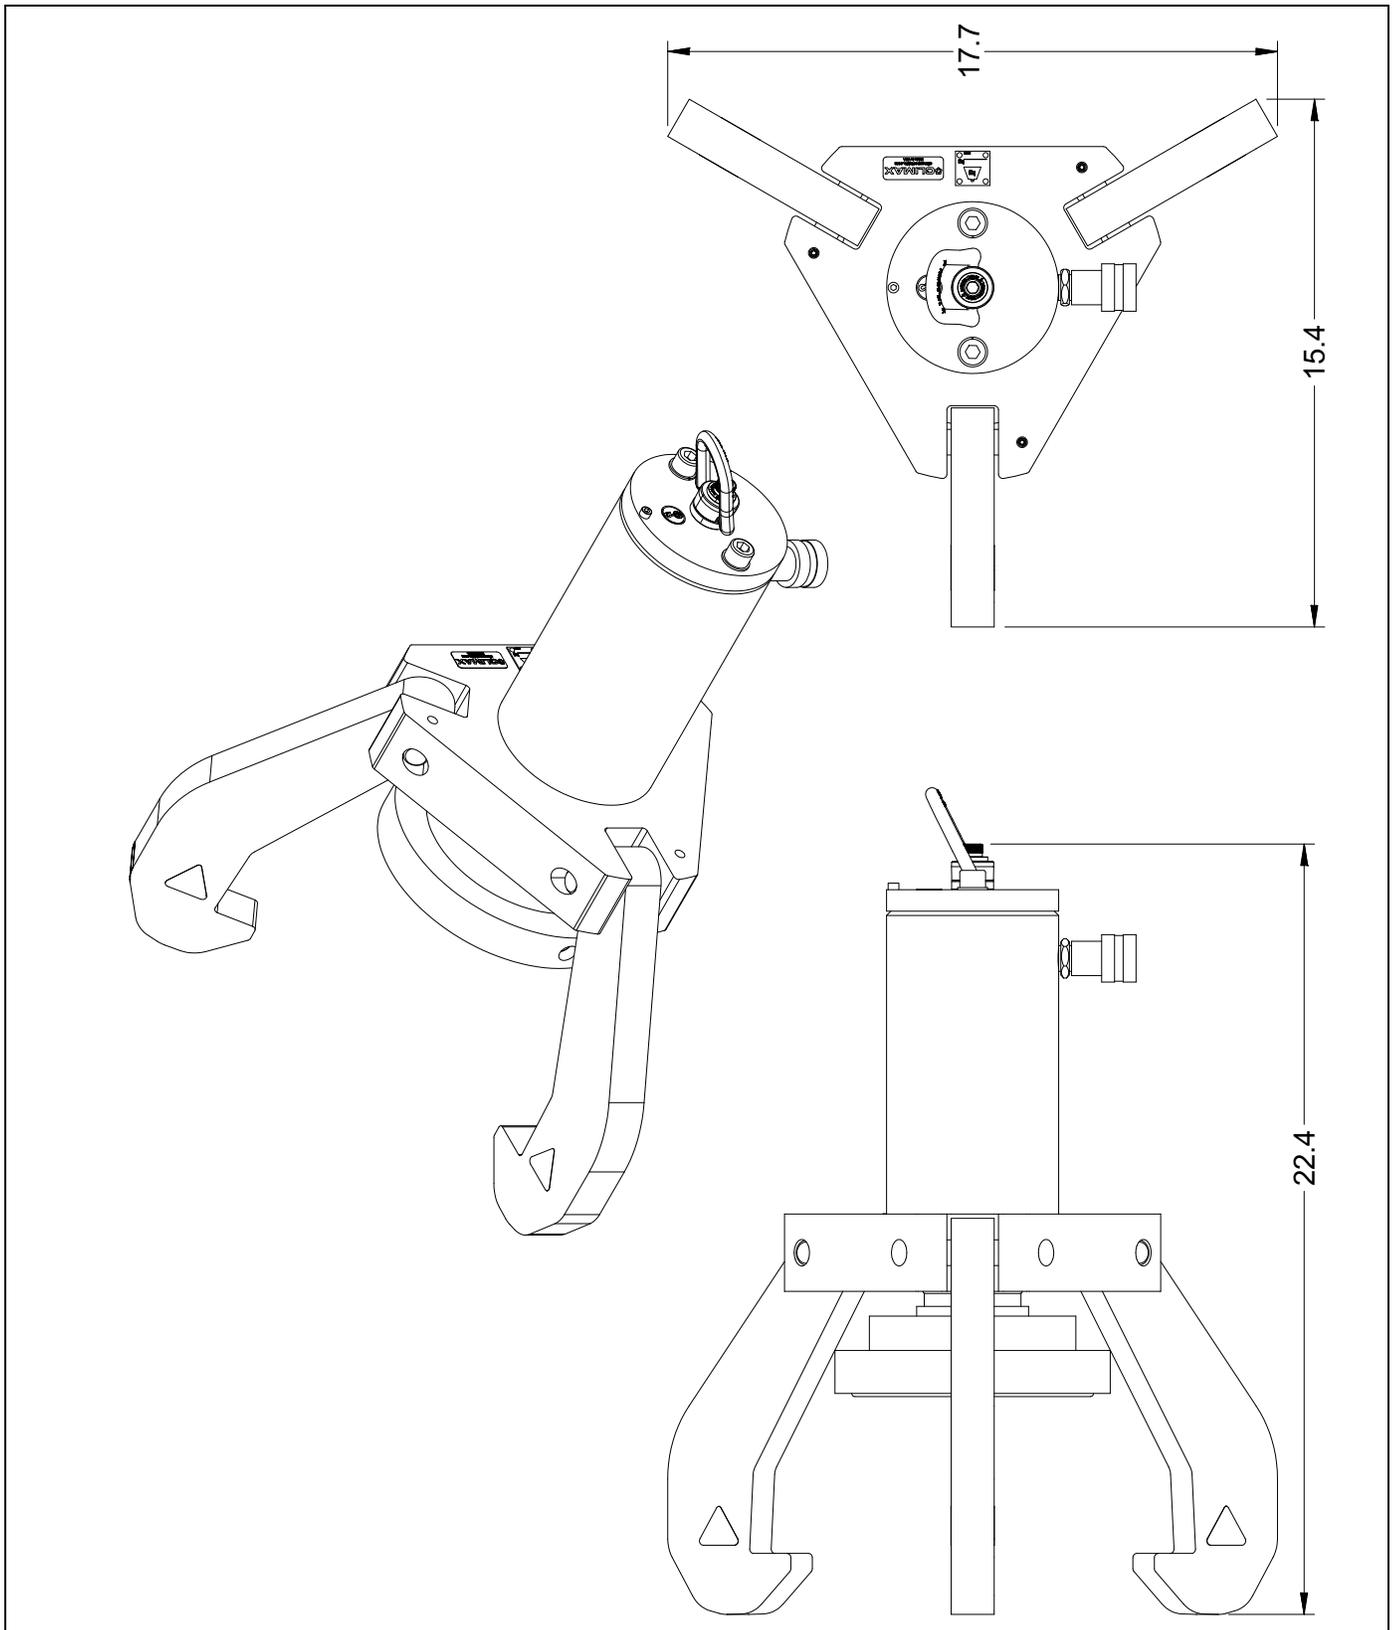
DIMENSIONS DE LA HFS-6
